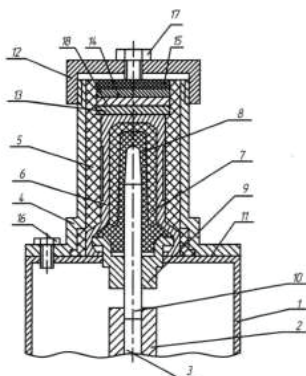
Конструктивный чертеж регулятора с твердым наполнителем и электронагревателем:
